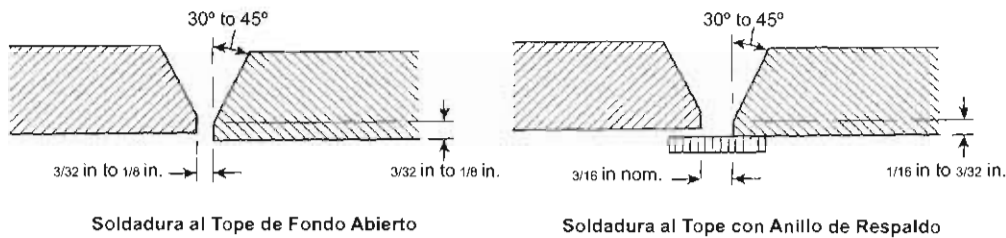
Diagrama de Soldadura
